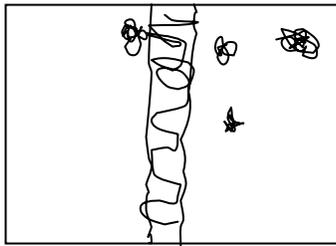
Cordón irregular en que se aprecian además pegotes y proyecciones de soldadura.
